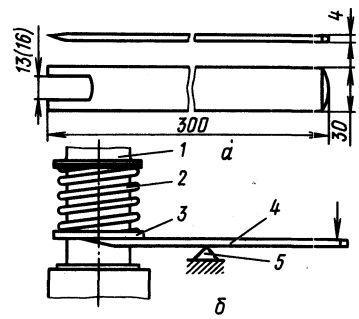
Устранение течи масла через уплотнители кожухов штанг двигателя МеМЗ:
